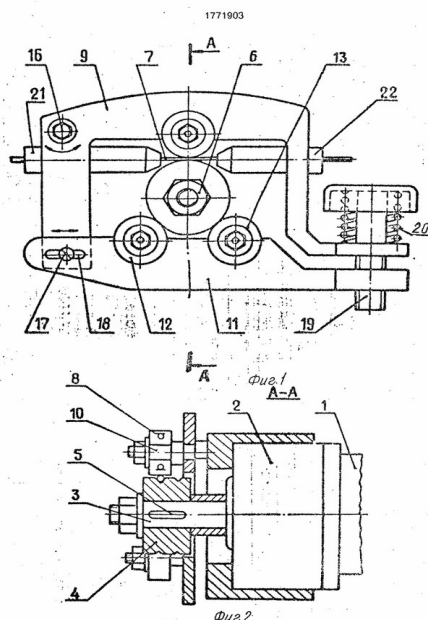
Механизм подачи сварочной проволоки
